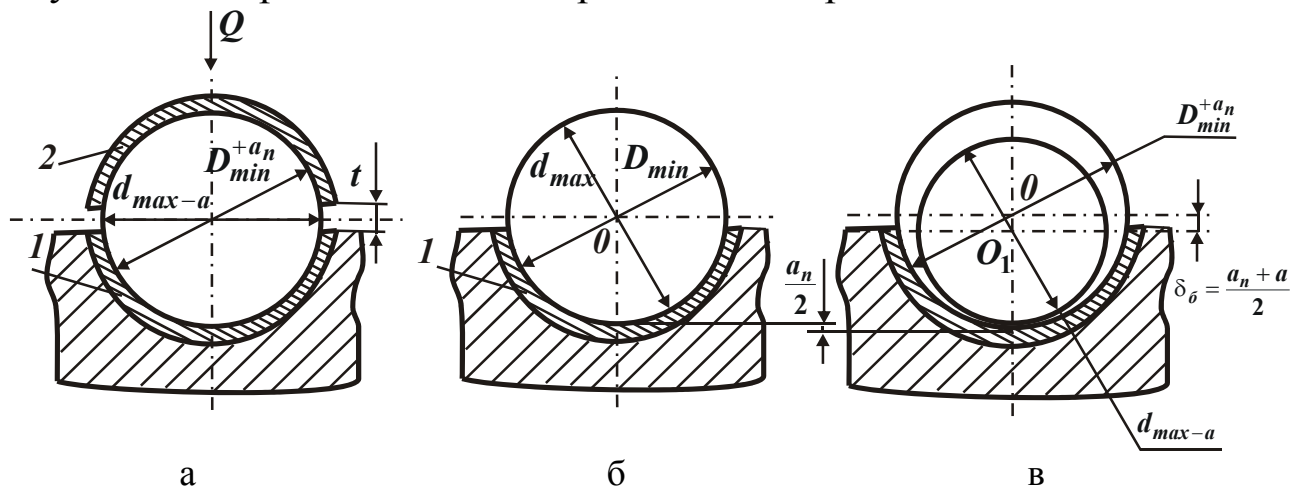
Схема базирования заготовки с главной базой, имеющей вид цилиндрической наружной поверхности, с помощью двух полуотверстий.
